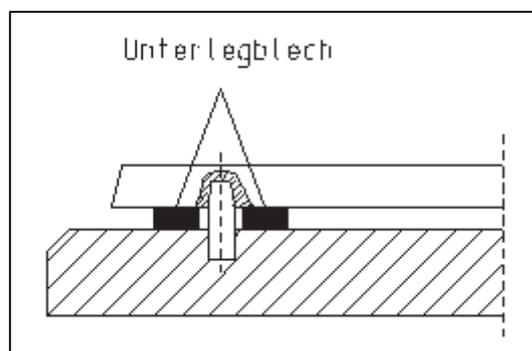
Befestigungsmaterial für Pumpe mit freiem Wellenende
